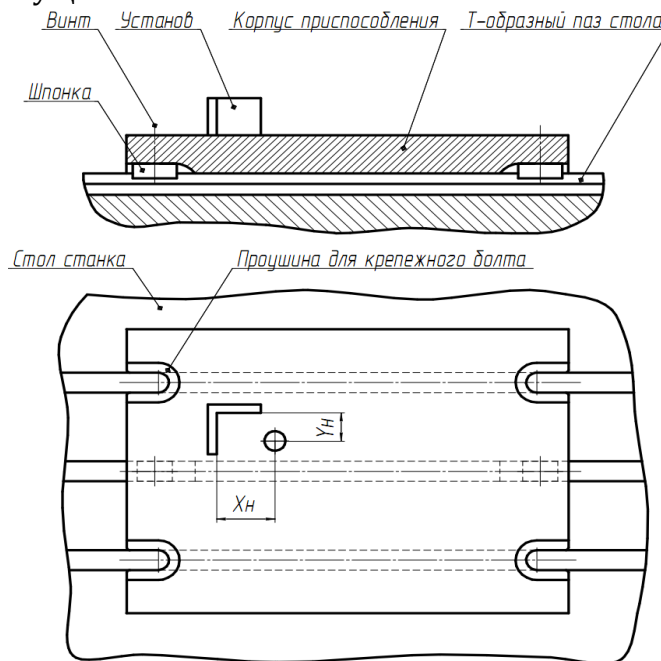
Базирование приспособления на столе станка по шпонкам и продольному пазу
